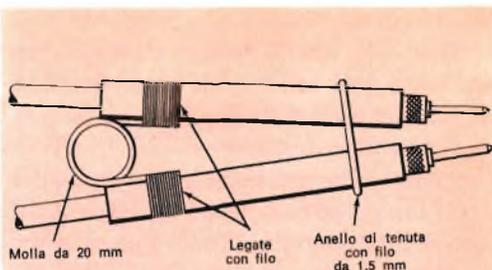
Un complesso di elettrodi a molla può essere realizzato fissando i manici ad una molla.
